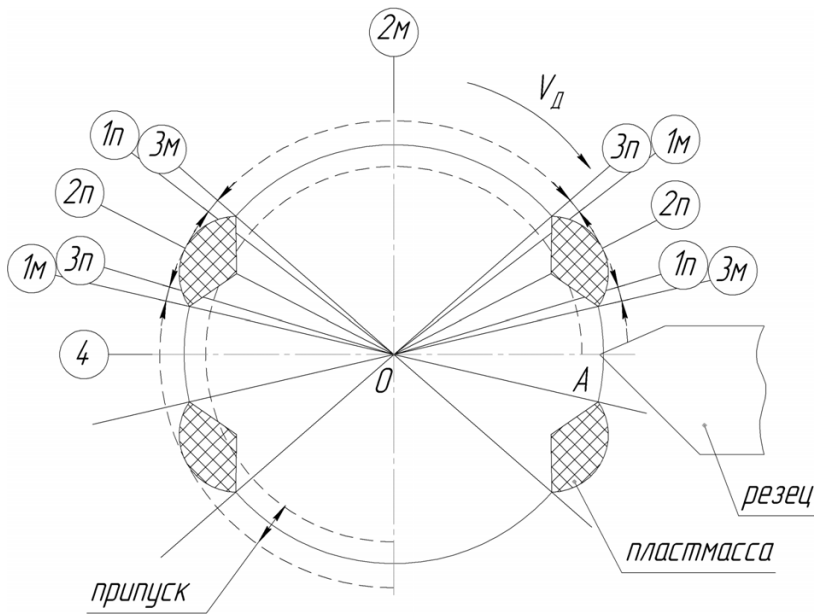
Схема обработки поверхности из двух конструктивных материалов (п – пластмасса, м – металл)
